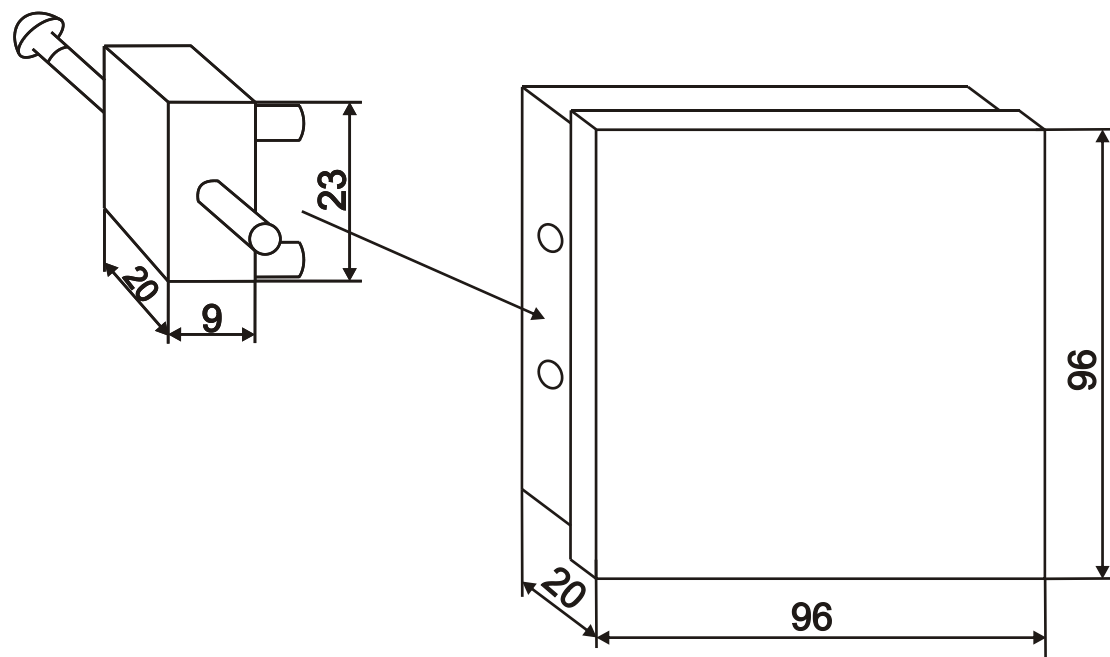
Способ крепления и габаритно-присоединительные размеры прибора
